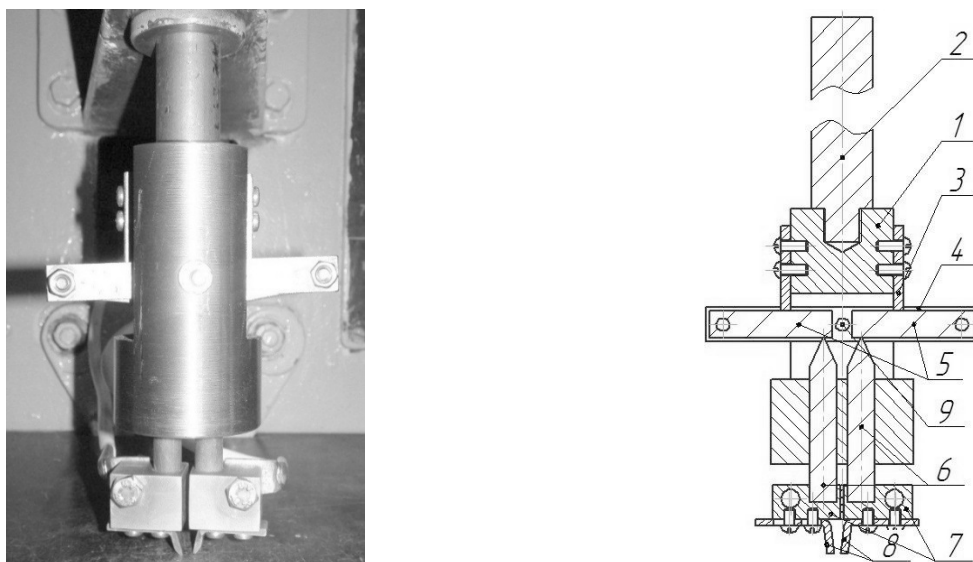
Модуль односторонней сварки: 1-корпус, 2-шток, 3-зуб, 4-коромысло, 5-рычаг, 6-палец, 7-электрододержатель, 8-электрод, 9-болт.
